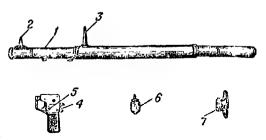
Основные части и механизмы ручного противотанкового гранатомета: 1— ствол; 2— мушка; 3— прицельная рамка; 4— ударно-спусковой механизм; 5— предохранитель спуска; 6— бойковый механизм; 7— предохранитель ствола
